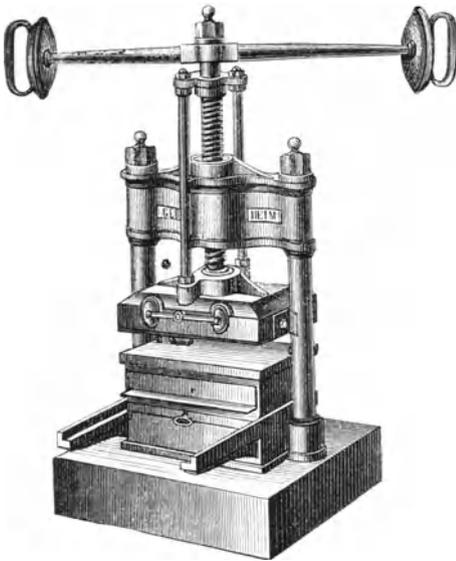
Vergoldpresse mit Schwen gel und hoher Einschleibeplatte aus der Maschinenfabrik der Gebrüder Heim in Offenbach.
